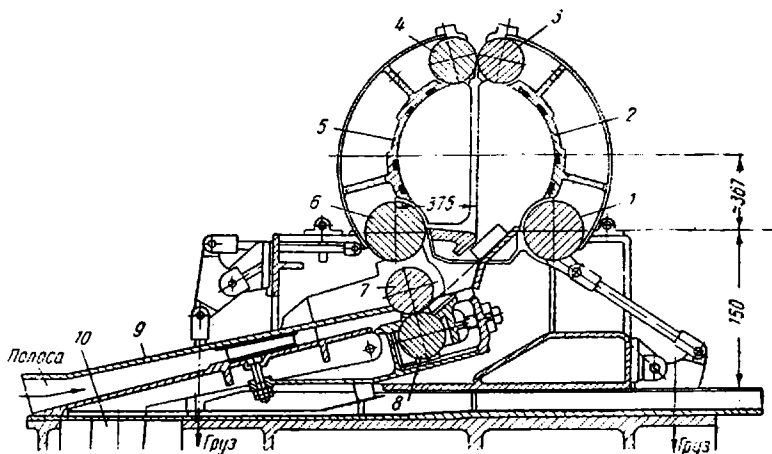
Свертывающая роliko-гибочная моталка для сматывания горячей узкой полосы (штрипса)
